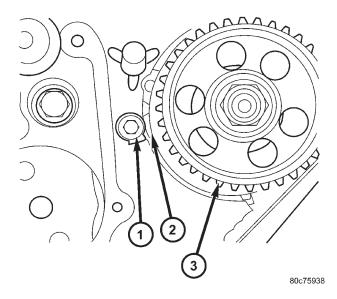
MARCAS DE REGLAJE DE ENGRANAJE DE BOMBA DE INYECCION
